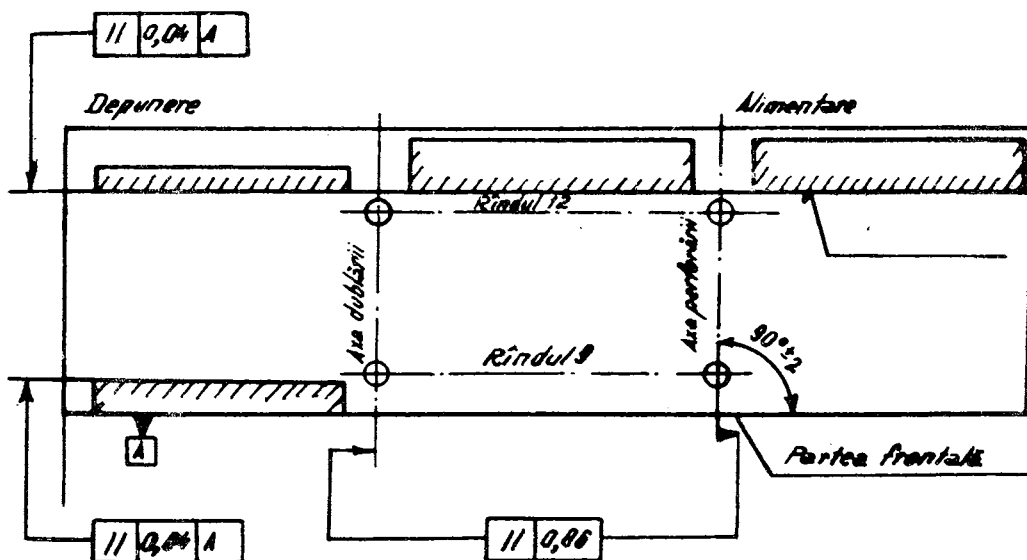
Exemple de toleranțe de poziție din mașina de perforat Soemtron 415.
